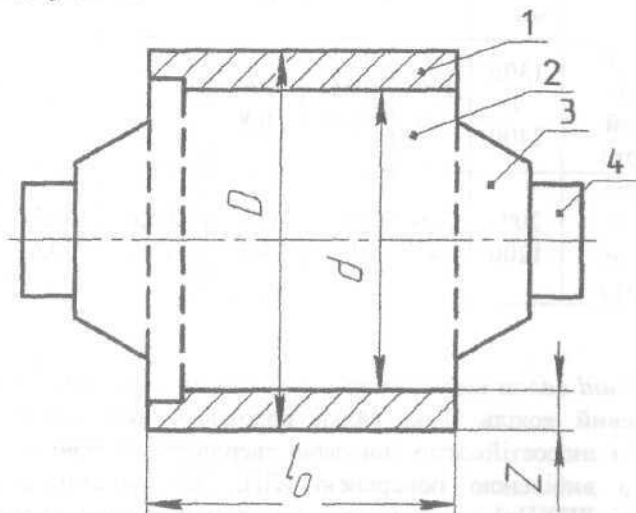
Складений опорний валок стана холодної прокатки штаб: 1 – бандаж; 2 – вісь; 3 – шийка; 4 – хвостовик
